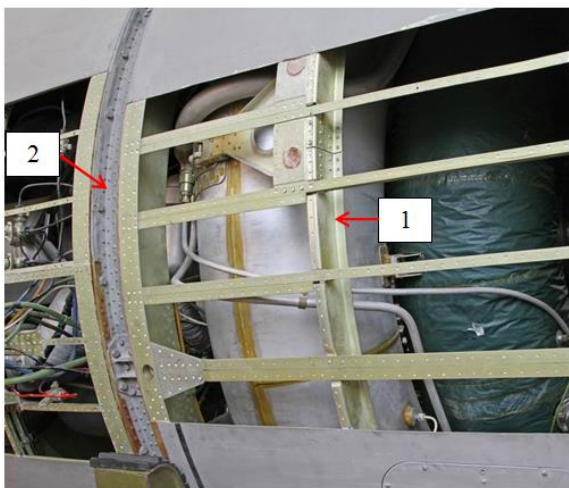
Фрагмент корпус ракетносителя, где 1 – шпангоут фюзеляжа ракеты; 2 – опорный шпангоут ракетного двигателя [54]
